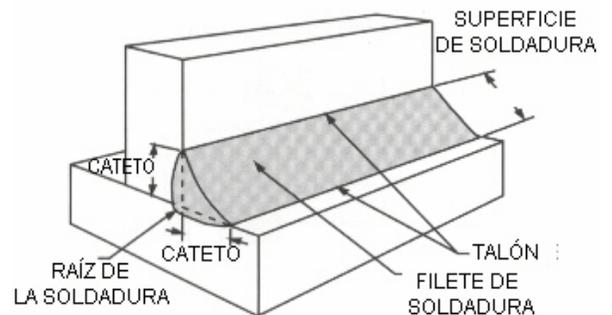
Terminología para soldadura de filete terminada
